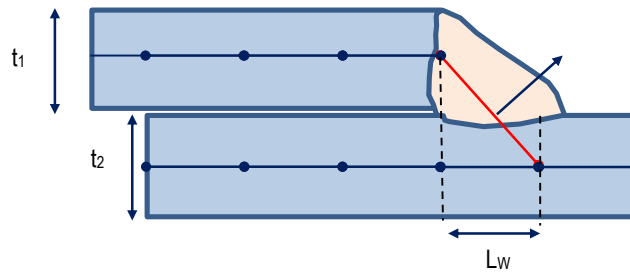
Overlap ve Laser Edge Overlap Weld İki Eleman ve Bir Eleman Yaklaşımı
